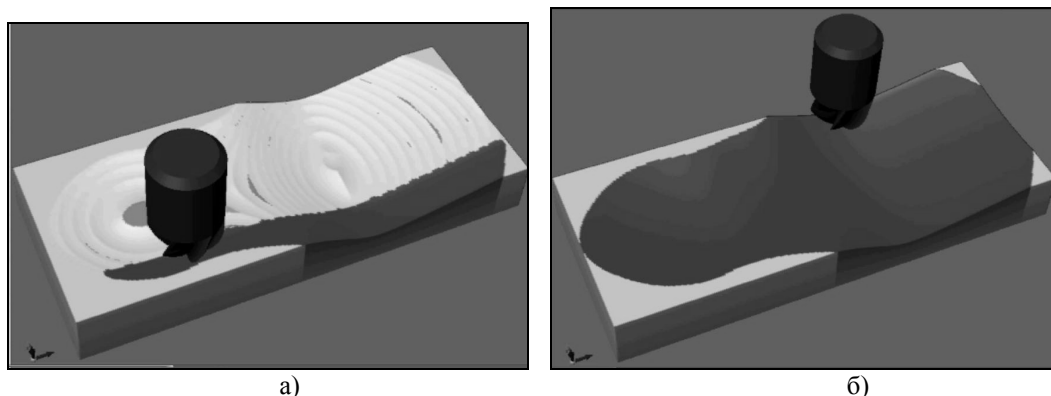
Комп'ютерне моделювання чистового порядкового фрезерування робочої поверхні пуансона ПФ в САМ-пакеті:
